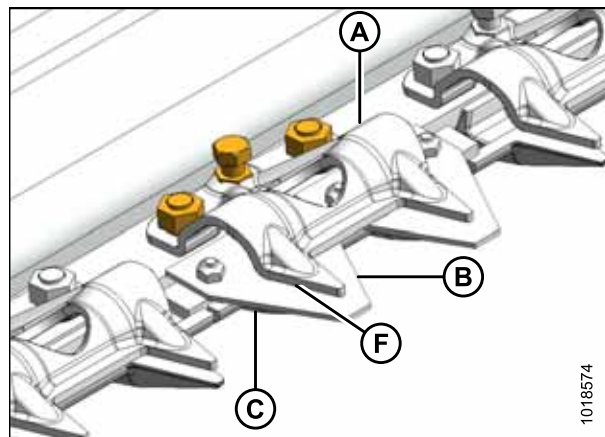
Стандартный прижим укороченного противорежущего пальца из листового металла
